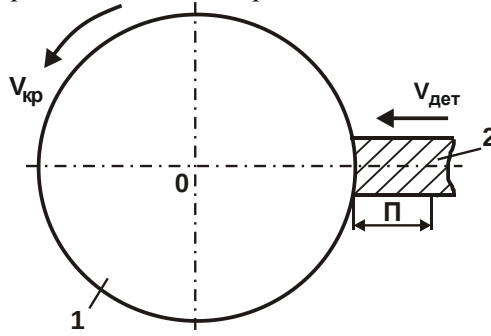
Расчетная схема параметров процесса шлифования прямолинейного образца, движущегося по нормали к рабочей поверхности круга: 1 – круг; 2 – деталь
